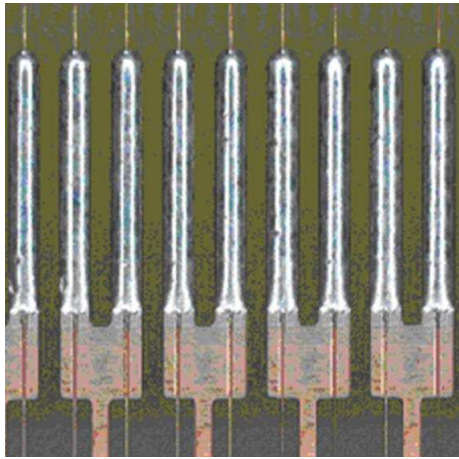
Detall de les soldadures dutes a terme amb el nou mètode
